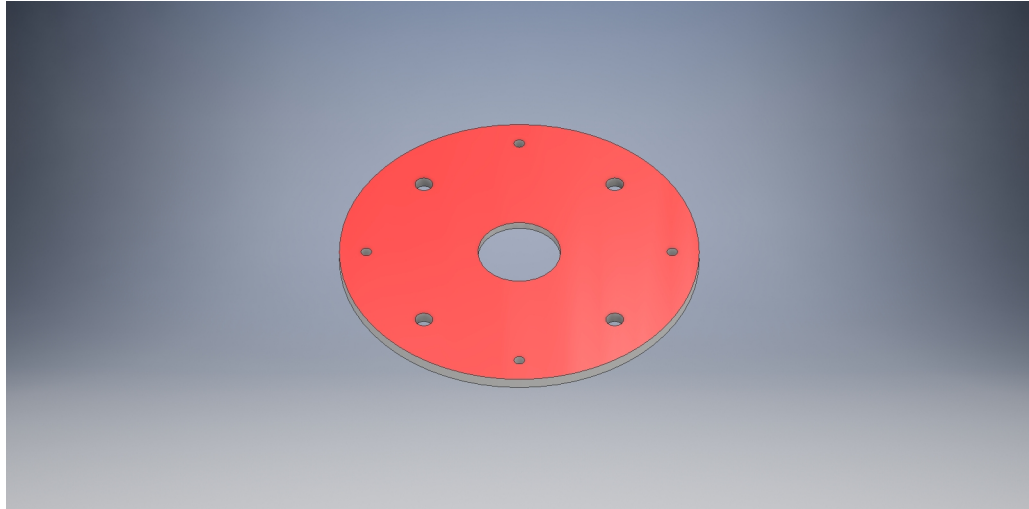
Parte superior del diseño mecánico del dispositivo esclavo
